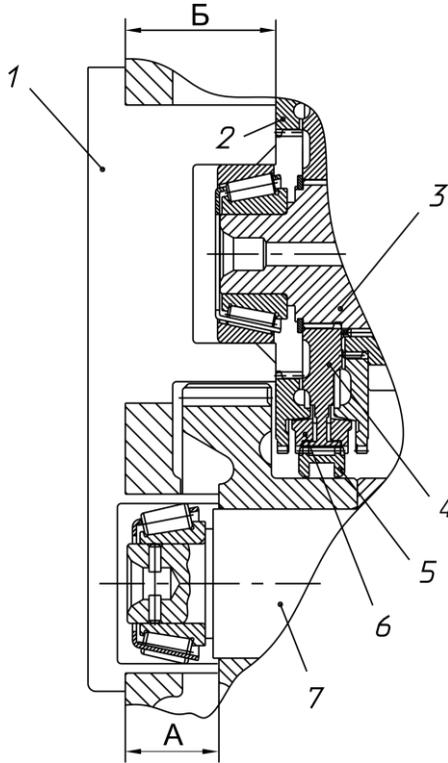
Установка промежуточного и вторичного валов в сборе:
